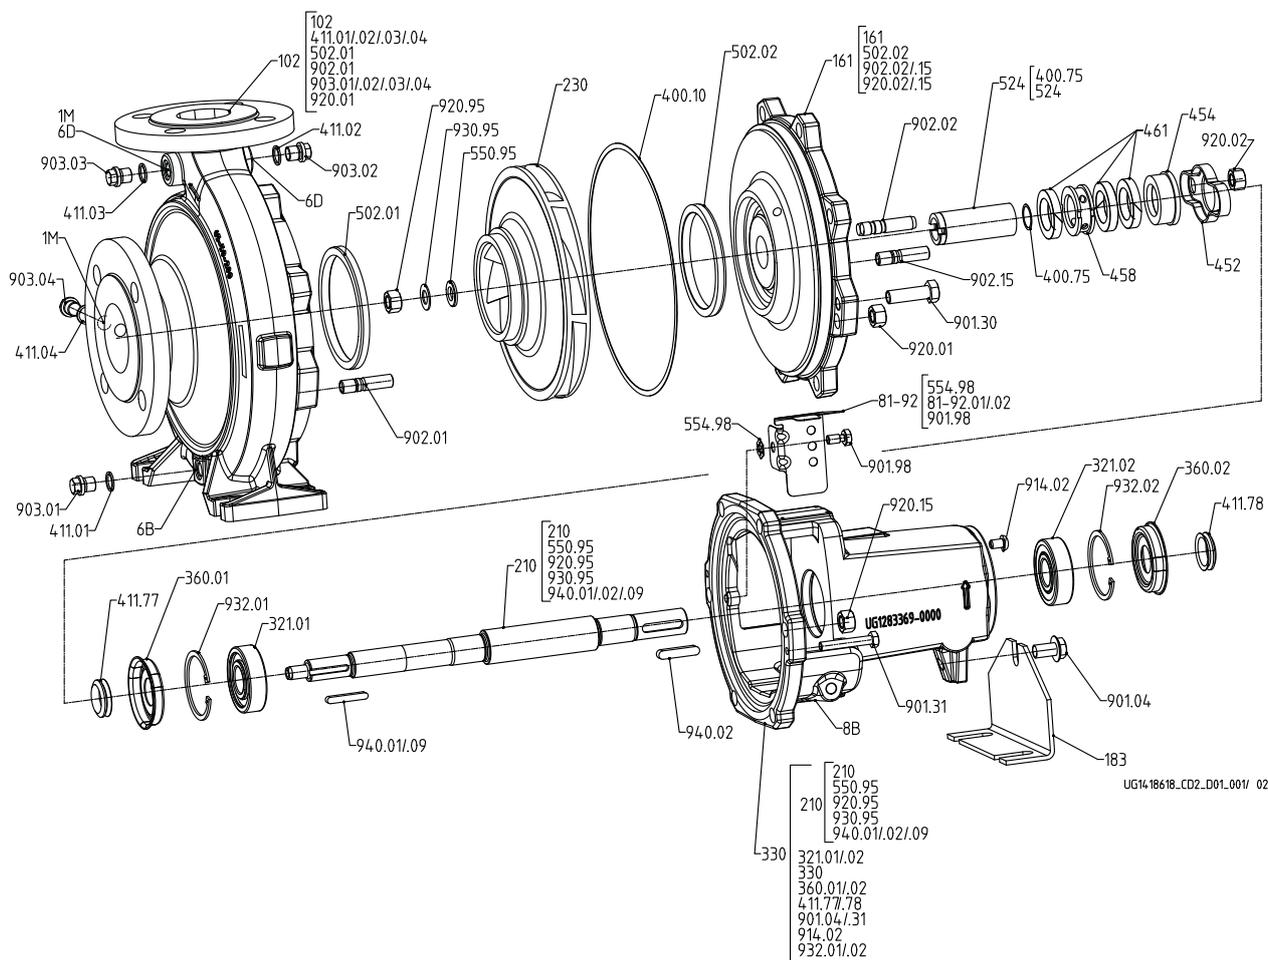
Исполнение с сальниковой набивкой и привинчиваемой крышкой корпуса
